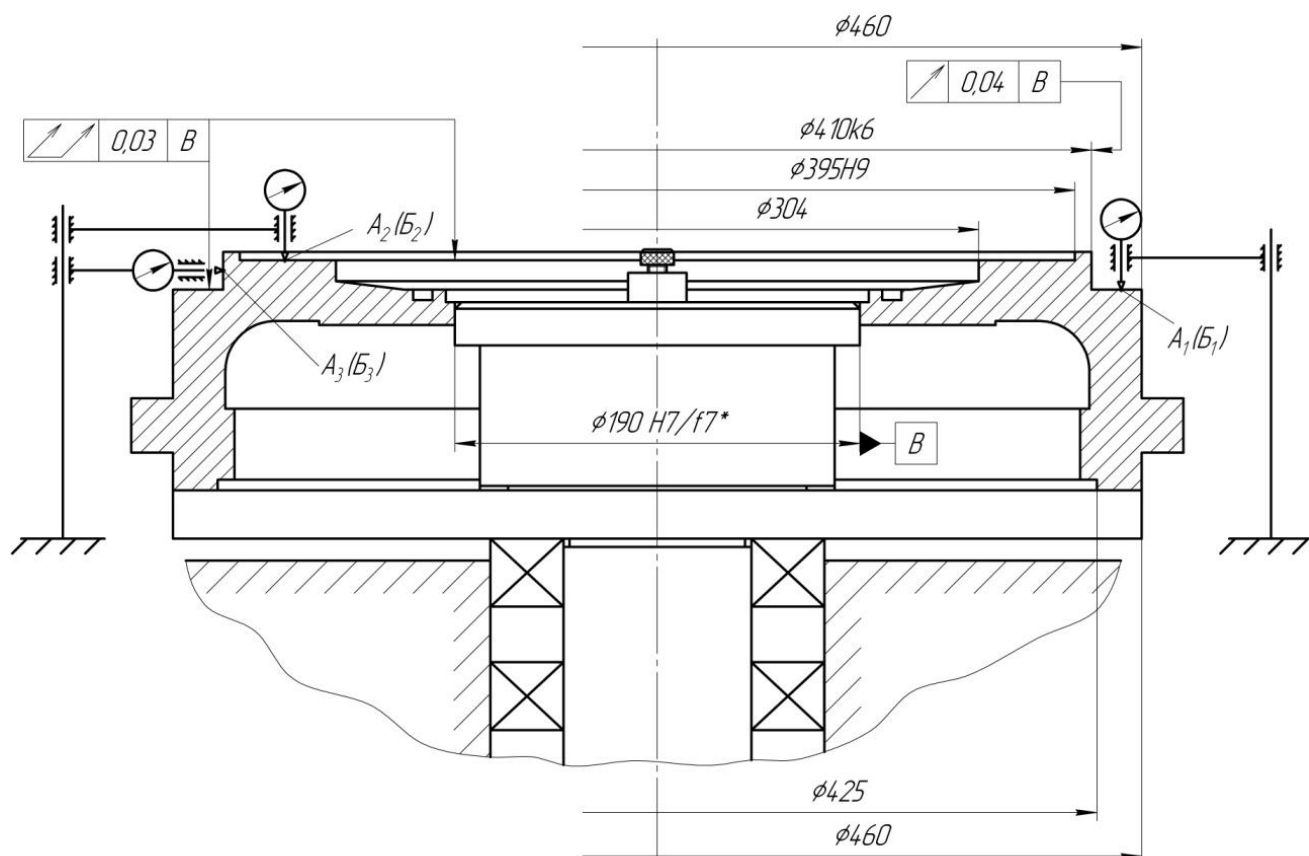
Схема вимірювання радіального биття поверхонь деталі
